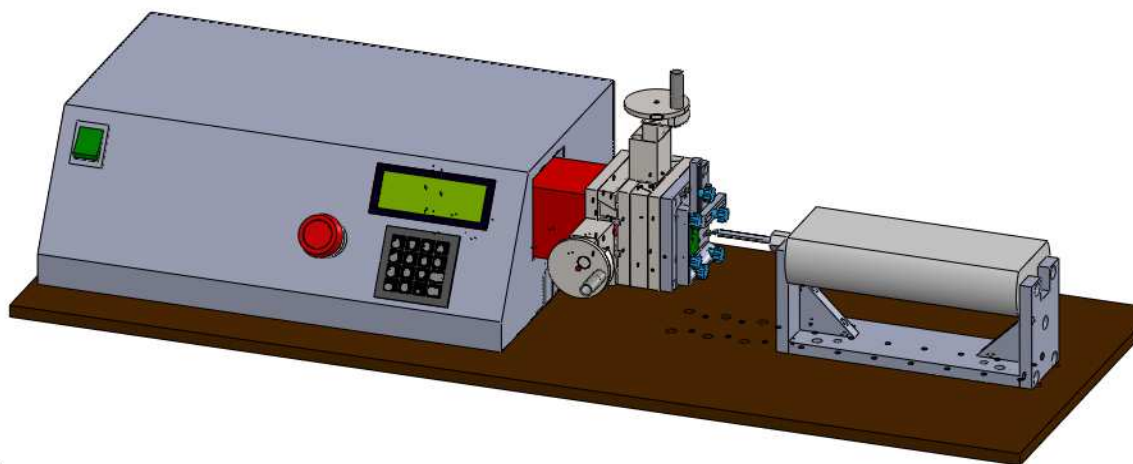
Vnitřní uspořádání měřidla TEST 321
